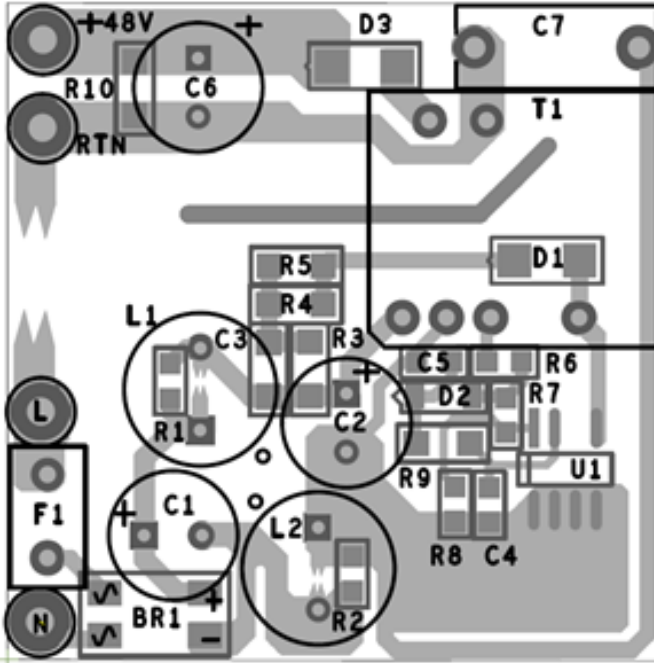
使用 SO-8C 封裝的 PCB 佈局範例。
